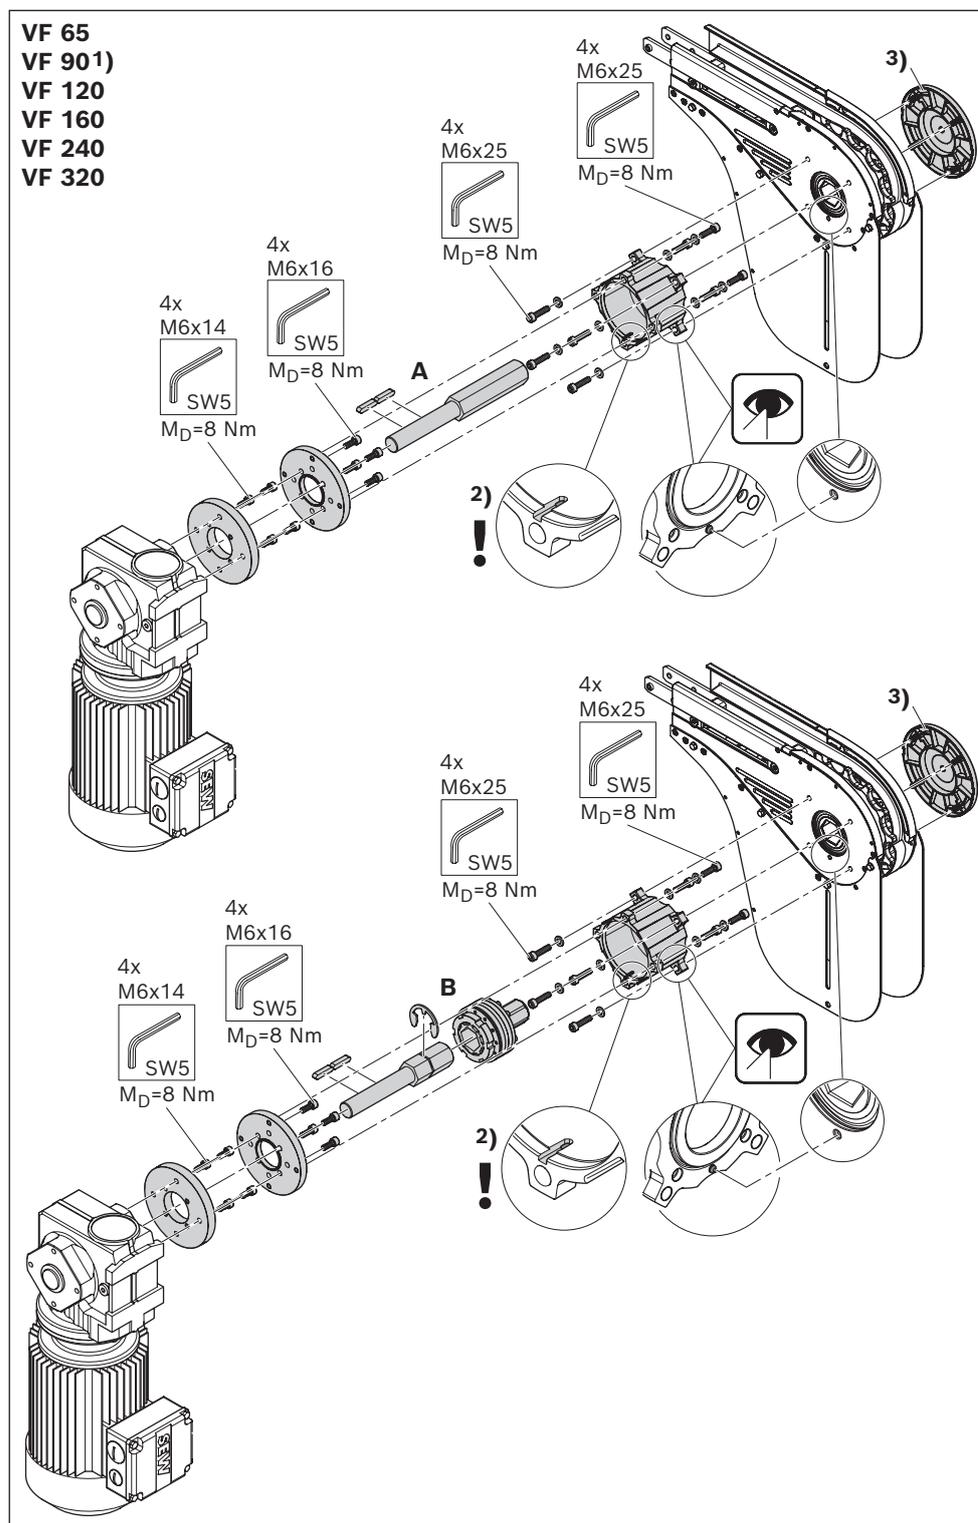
Montaje de la unidad básica, sistema AL, motor reductor GM = 4 con/sin acoplamiento
